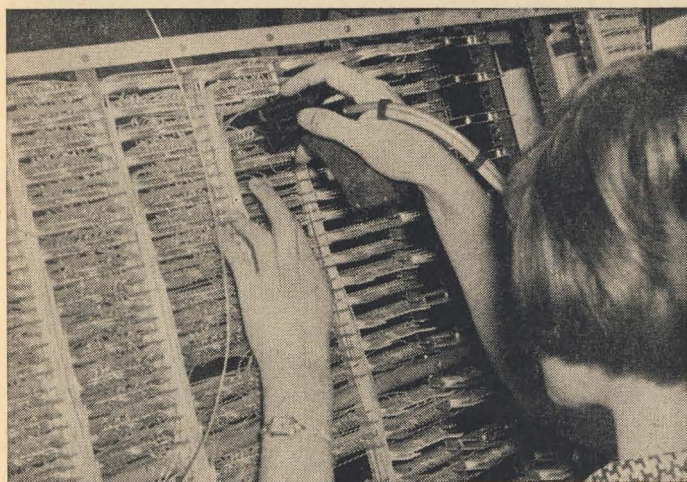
Die Rückverdrahtung in Form der Wickeltechnik
